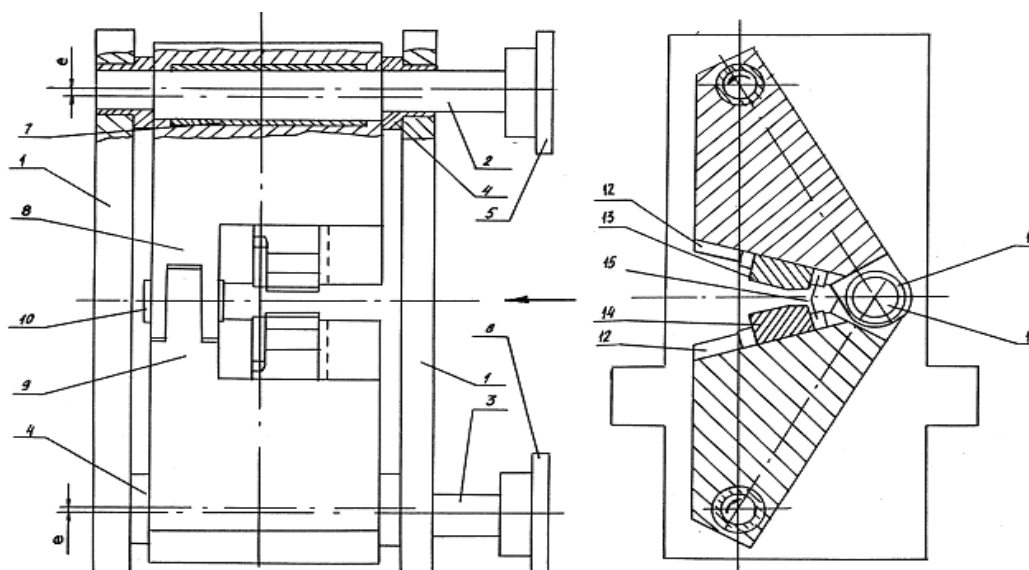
Ковочный блок установки совмещённых процессов непрерывного литья и деформации
